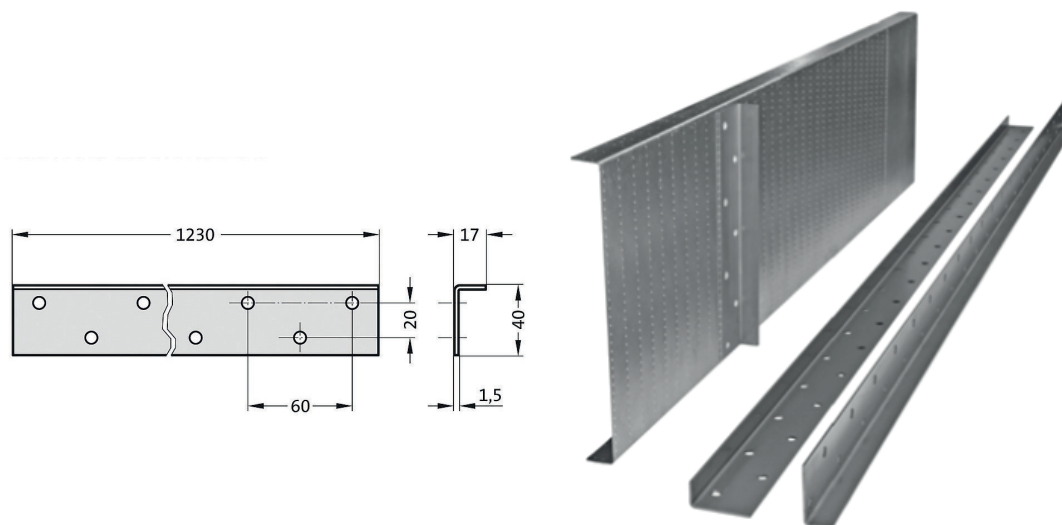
Kit de montage profil angulaire pour rail de blocage
